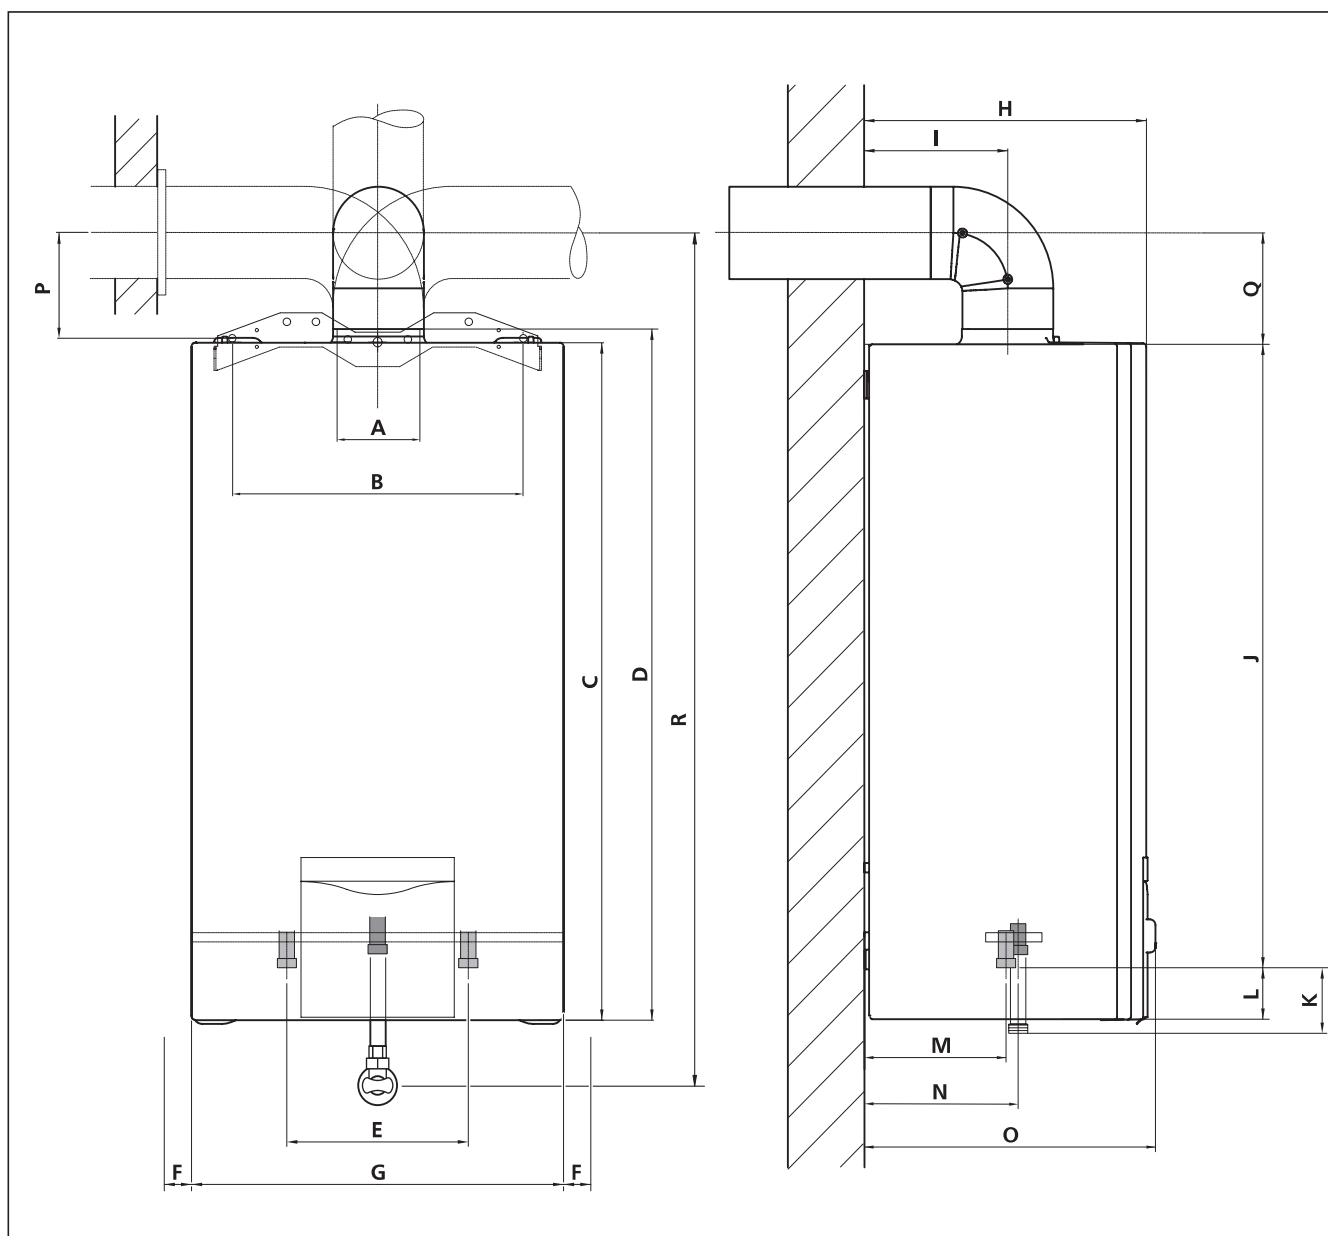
Чертеж с размерами turboMAG 16-2/0
